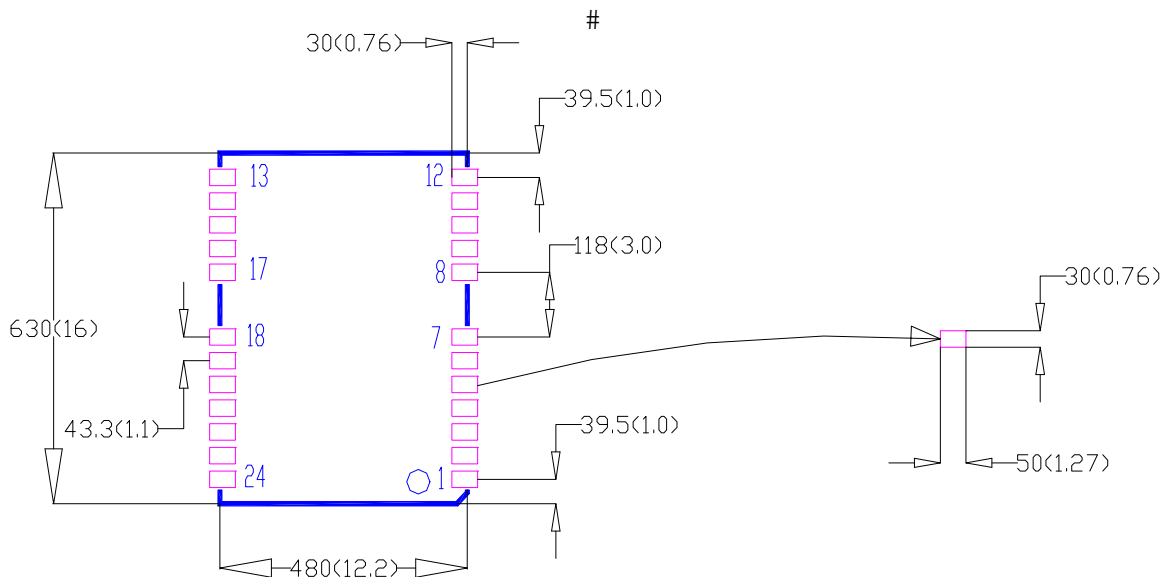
UM220-III N 推荐 PCB 封装设计 (尺寸单位: mil, 括号内单位: mm)
